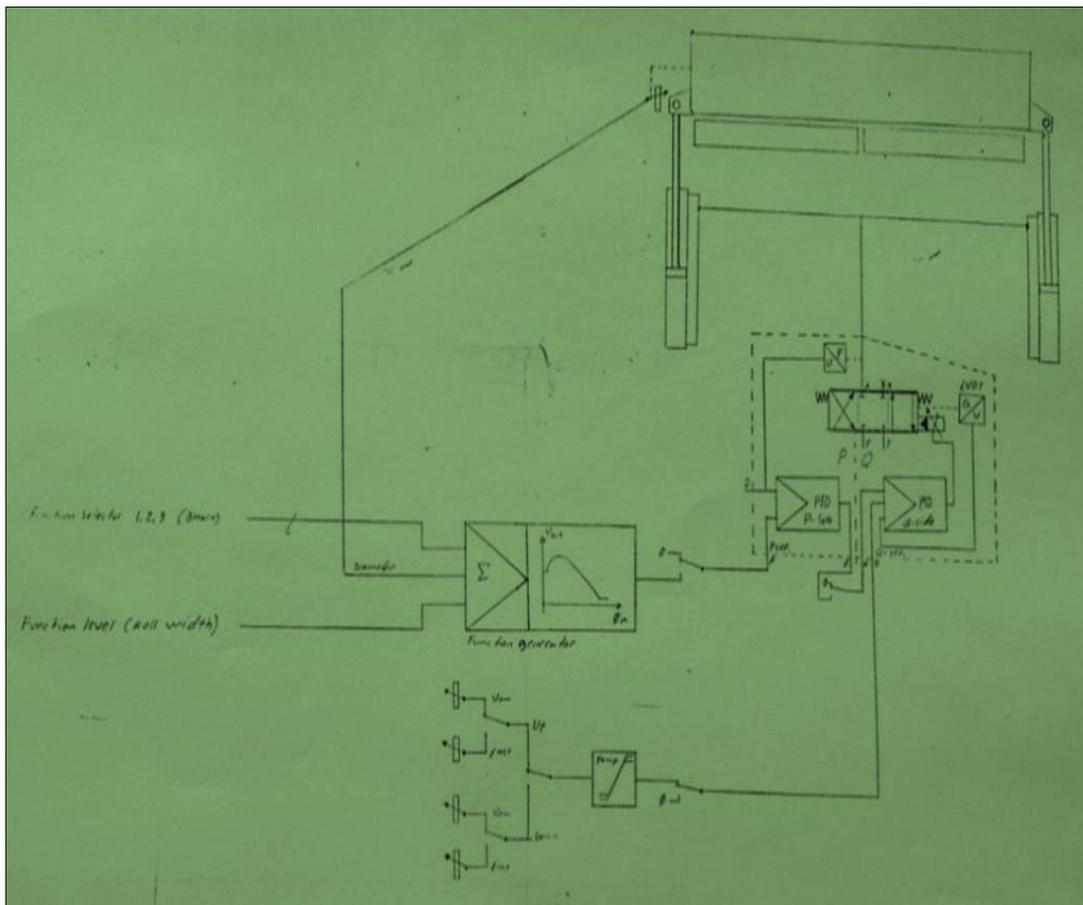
Control Electrohidráulico en el Rodillo Jinete.
